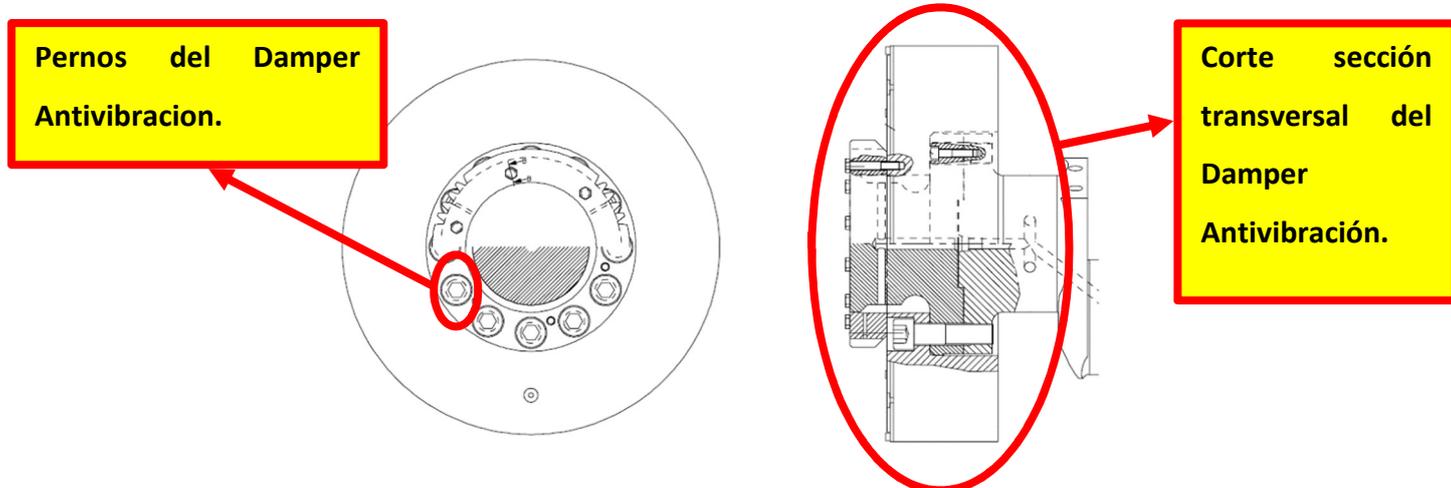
Detalle Damper Antivibración. Fuente: [8].
